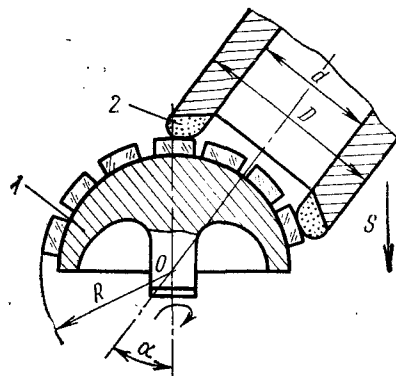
Шлифование блоков заготовок трубчатым алмазным инструментом
